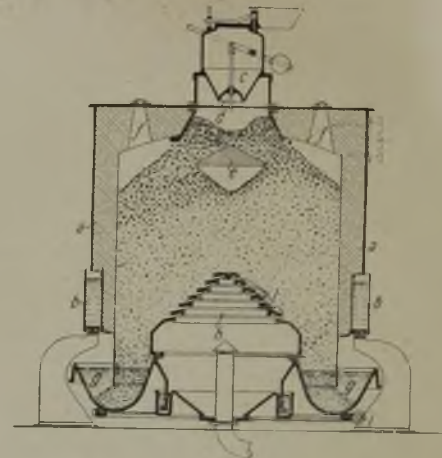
Längsschnitt durch den Generator der Augsburg-Nürnberger Maschinenfabrik. Maßstab 1:75.
